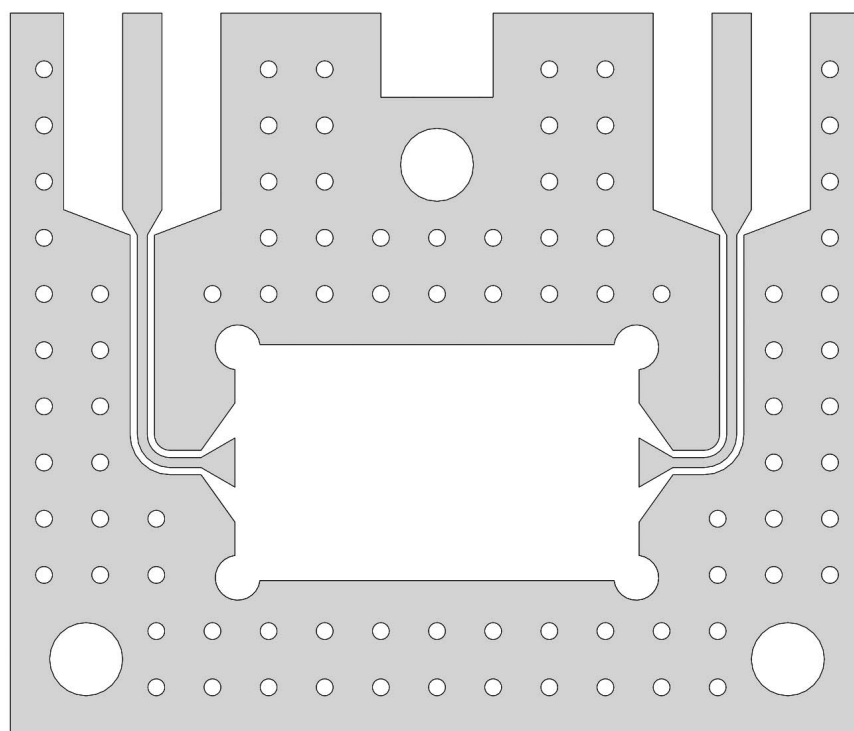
为新的竖直放置样品的样品盒所设计的 PCB 板
